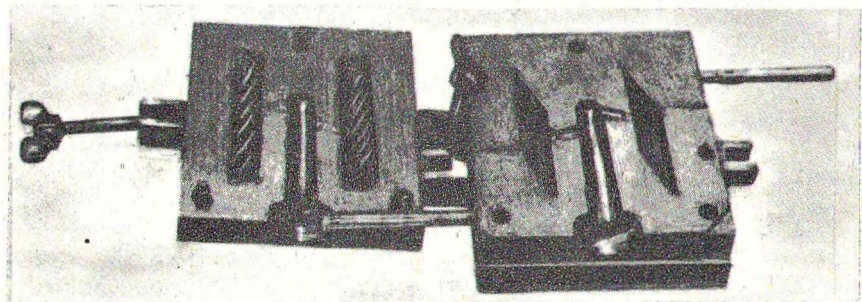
Кокиль для отливки секций с рифленным ручьем.
